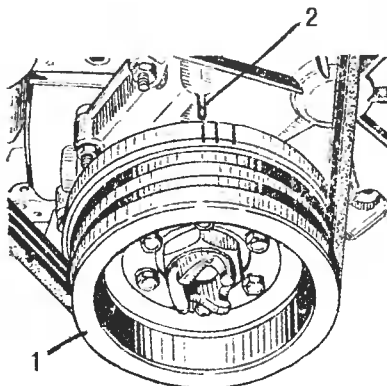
Метки на шкиве коленчатого вала для установки поршня первого цилиндра в ВМТ и установки момента зажигания:
